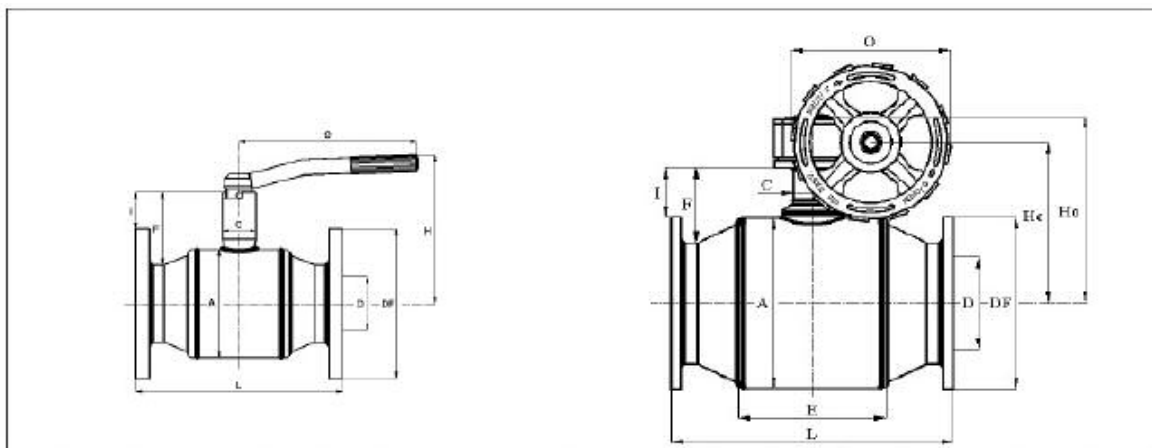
Габаритные и присоединительные размеры кранов шаровых типа LD с рукояткой и патрубками под приварку.
